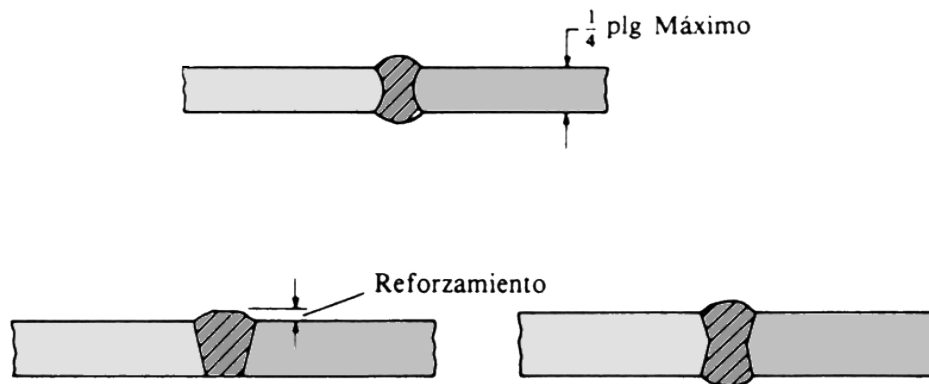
Soldadura de ranura. Nota. Datos tomados de <http://webdelprofesor.ula.ve/nucleotrujillo/americanab/07-conexionessoldadas/7-11.html>
